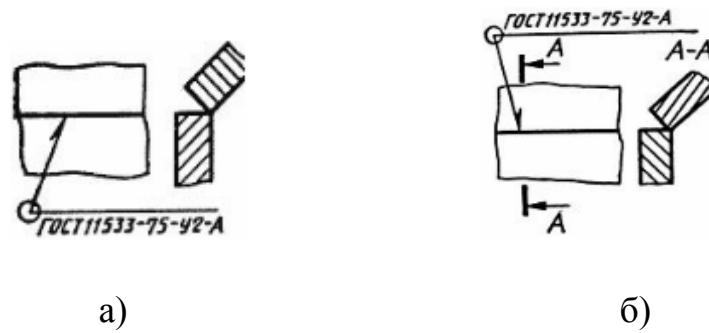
Пример условного обозначение сварочных швов на чертеже по ГОСТ 2.312-72, где а - с невидимой стороны, б - с видимой стороны
